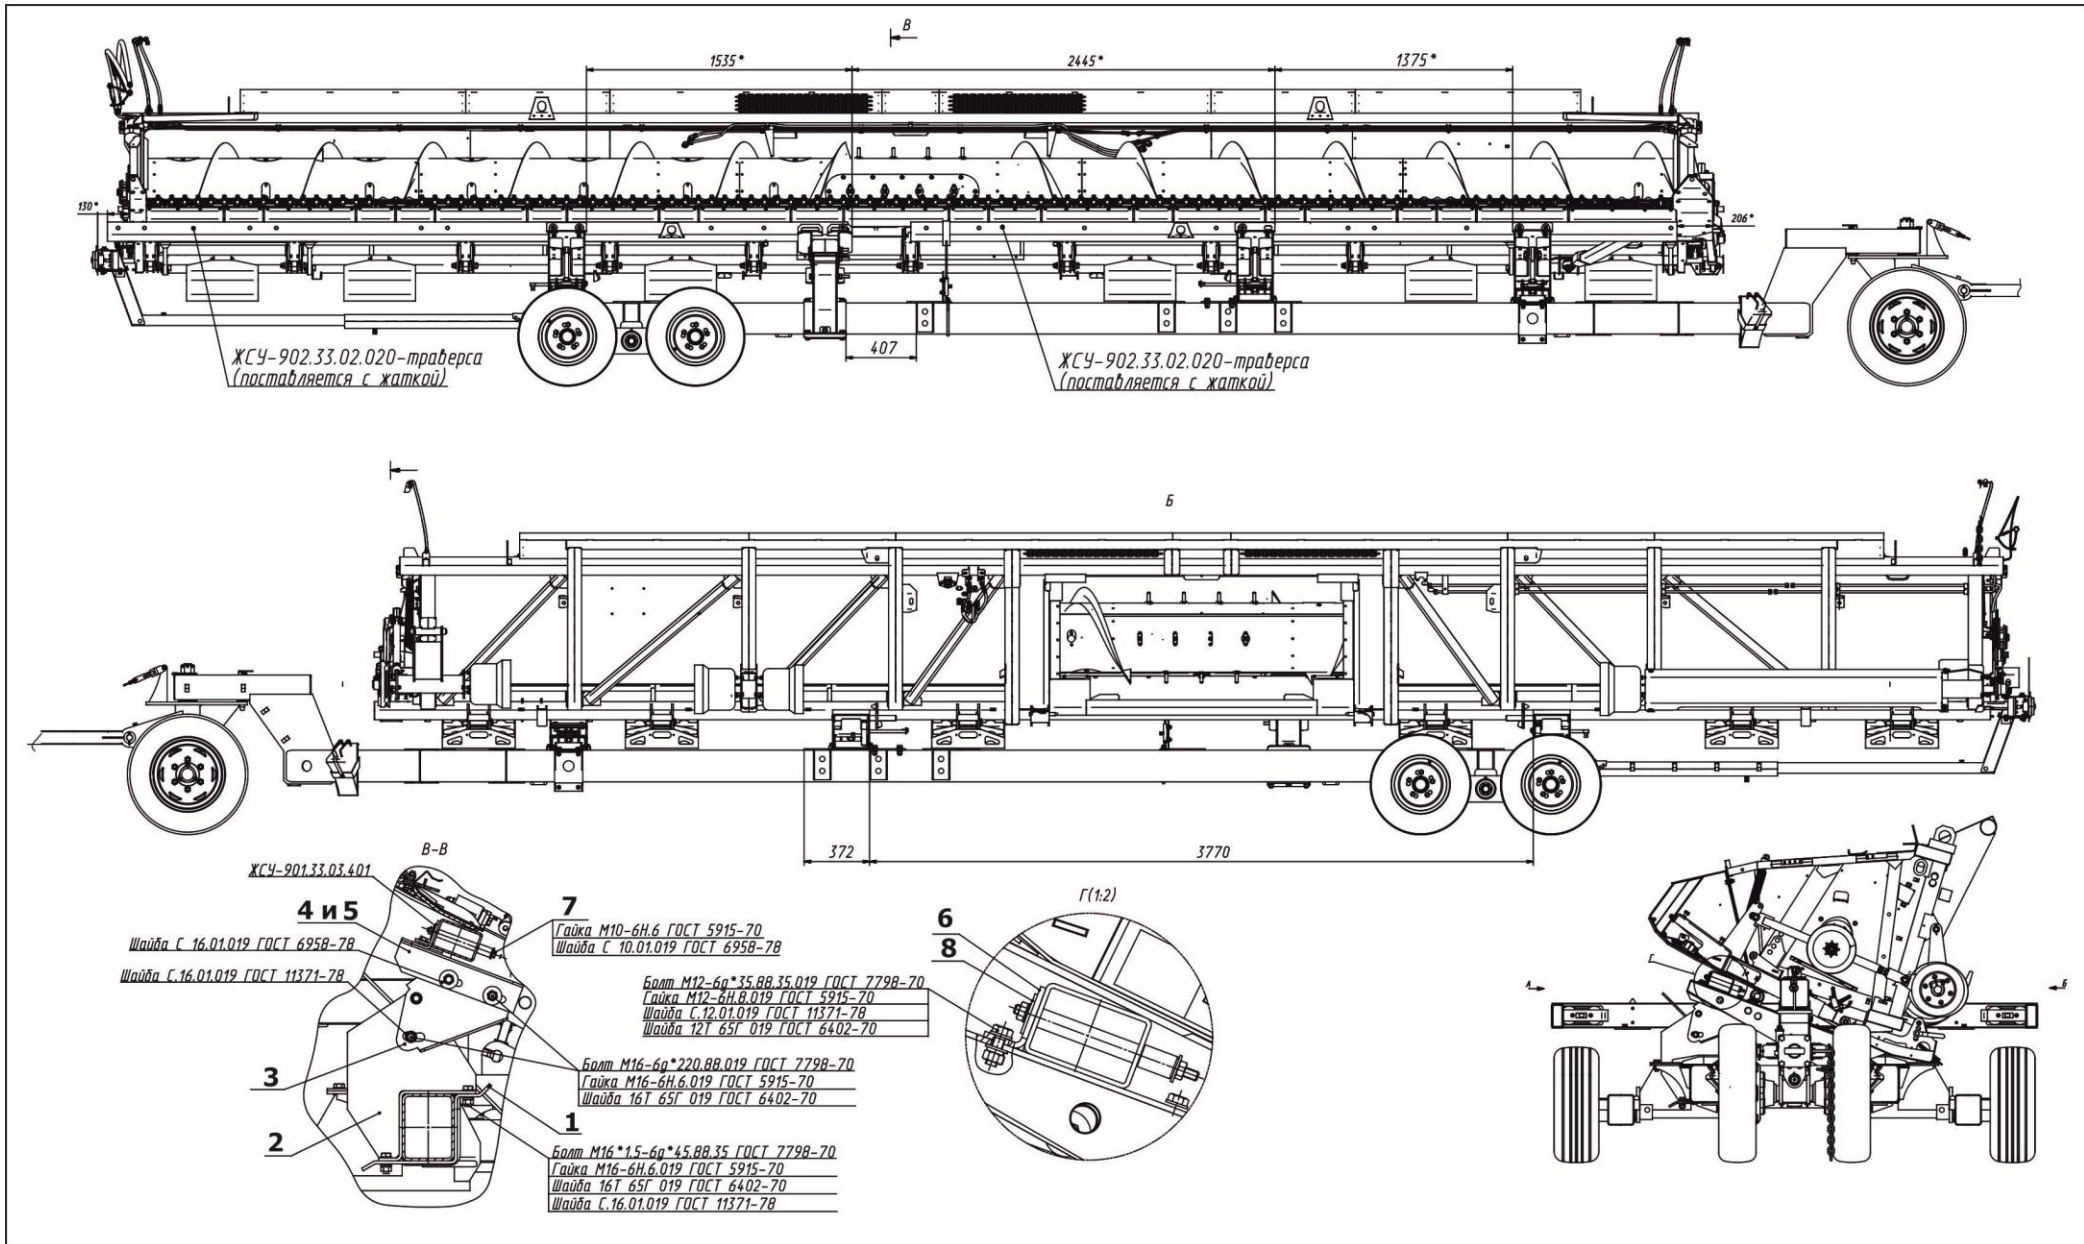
Схема установки комплекта FS-902.33.00.000 на приспособление ППА-4000-05
